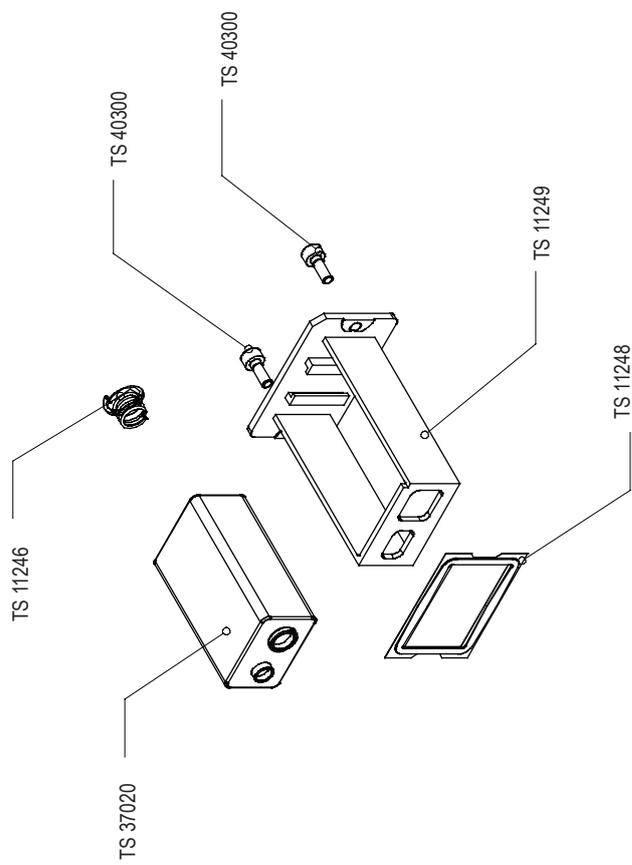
держатель батареи в сборе TS 10189, детали
